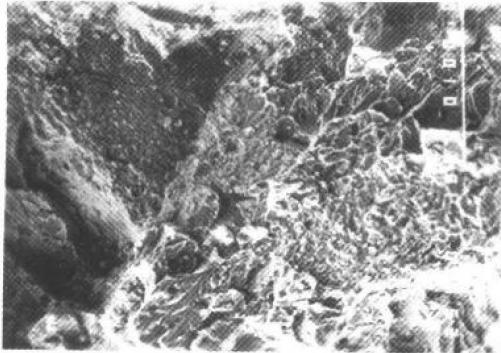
弧裂宏观断口(照片 2-4a)中部的微观准解理断裂花样,600×(SEM)
